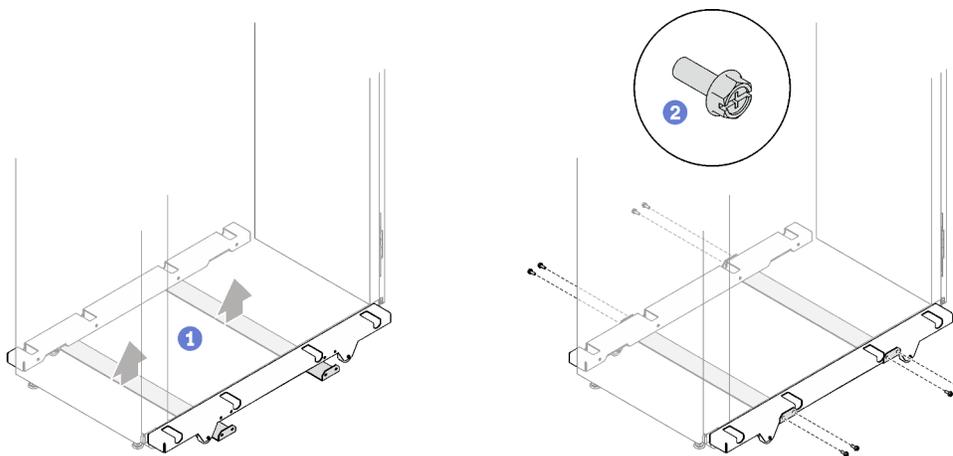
Installazione delle barre stabilizzatrici degli stabilizzatori
